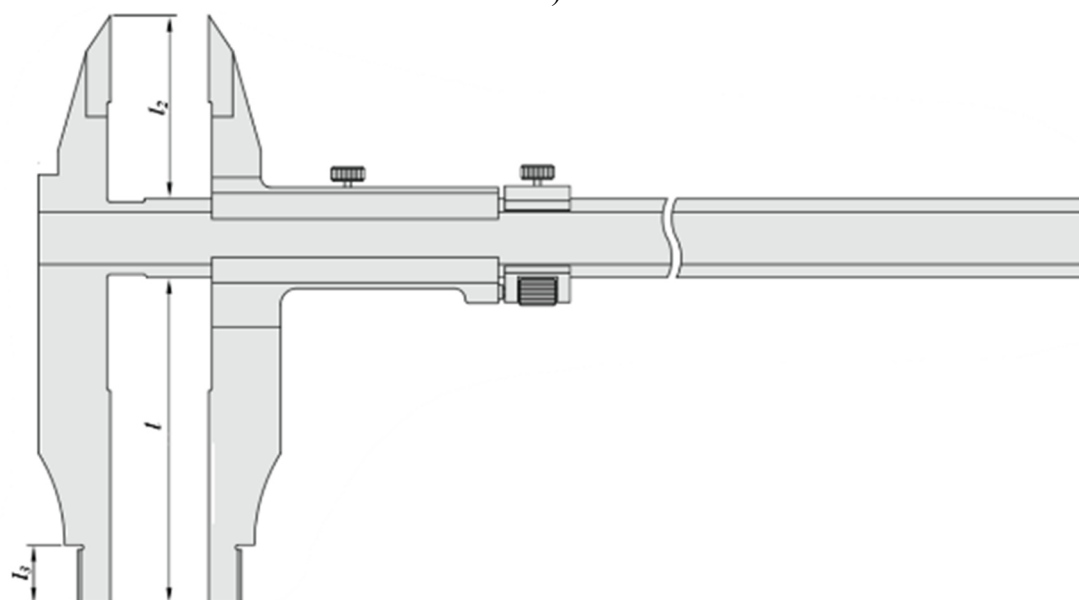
Общий вид штангенциркулей модификаций 126, 127, 128
